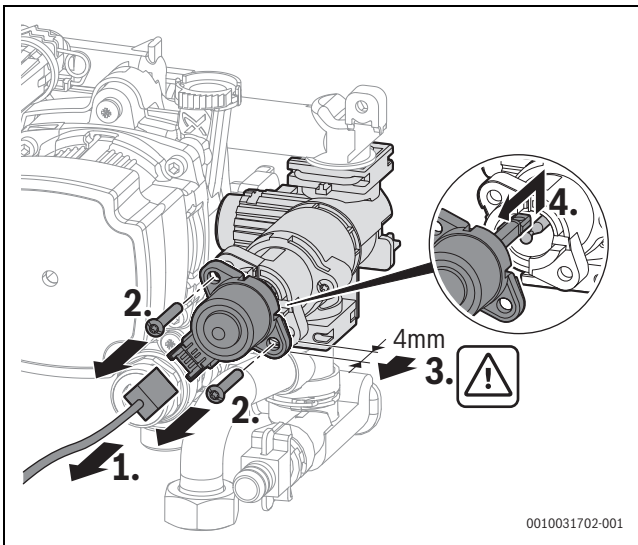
Motor am 3-Wege-Ventil ausbauen (Variante mit Schrauben)
